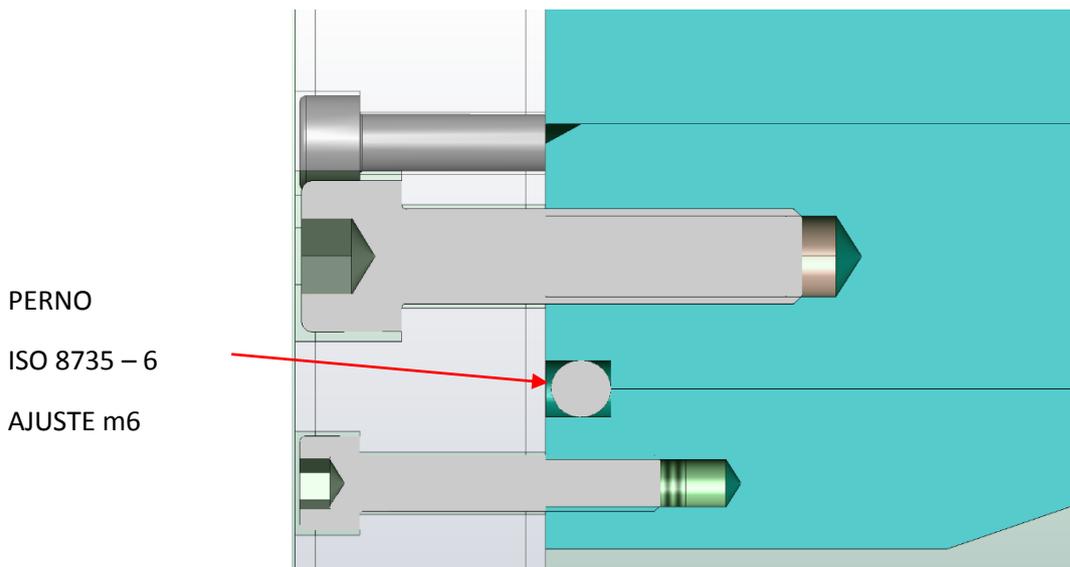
CAD Corte de sección de sistema anti giro
